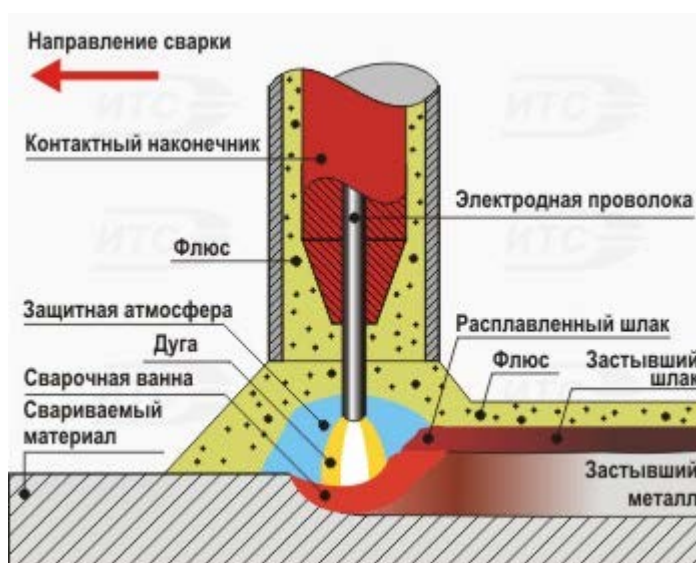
Схема автоматической дуговой сварки под флюсом
